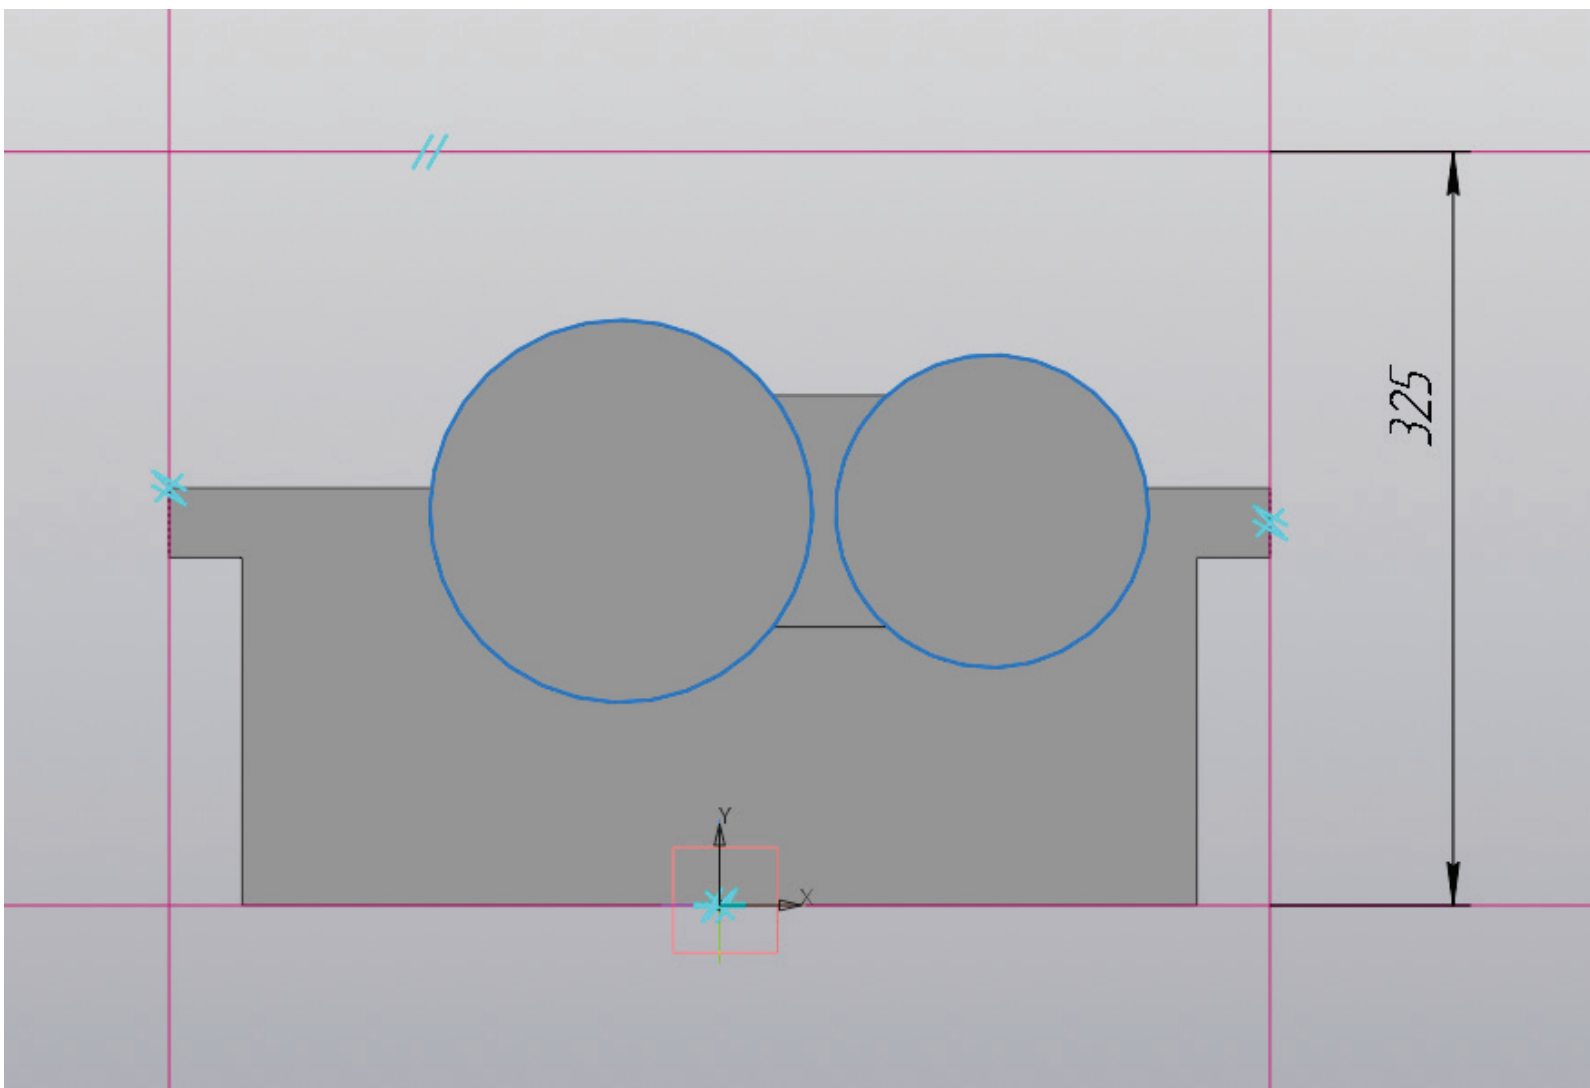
Работа с эскизом, создание верхней части редуктора
